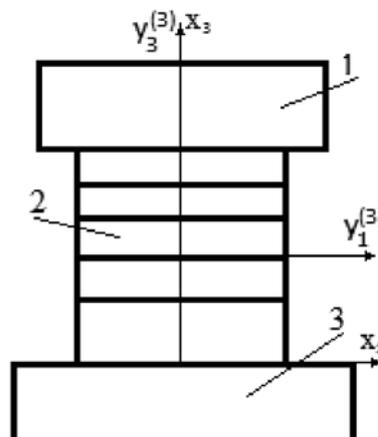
Схема напряженно-деформированного состояния при осадке многослойного параллелепипеда: 1 – верхний штамп; 2 – заготовка; 3 – нижний штамп
